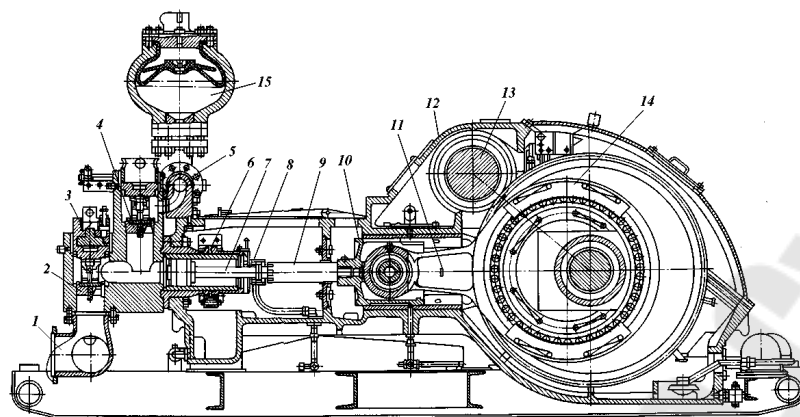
Буровой поршневой насос одностороннего действия: 1 - всасывающий коллектор; 2, 4 - всасывающий и нагнетательный клапаны; 3 - крышка клапанной коробки; 5 - нагнетательный коллектор; 6 - цилиндрическая втулка; 7 - шток; 8 - быстросъемный хомут; 9 - контршток; 10 - ползун; 11 - шатун; 12 - станина насоса; 13 - трансмиссионный вал; 14 - коренной вал; 15 - пневмо-компенсатор
